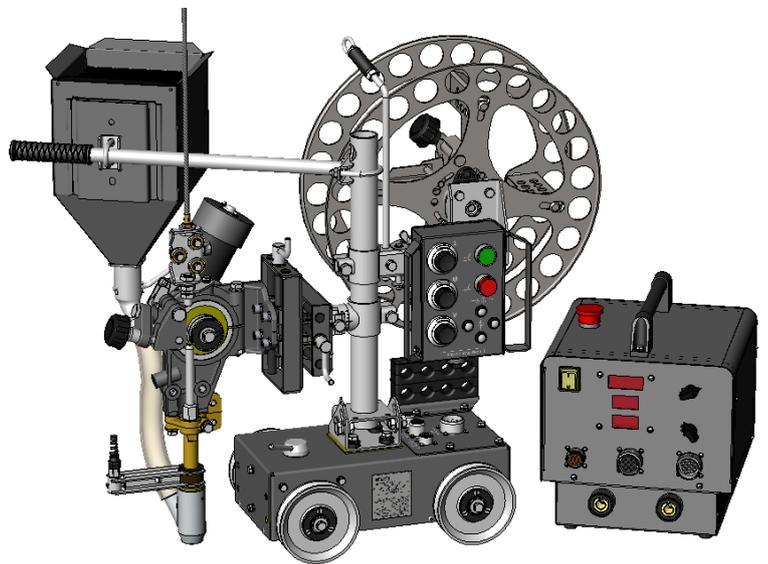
Автомат сварочный АДГ-630 исп.-04
